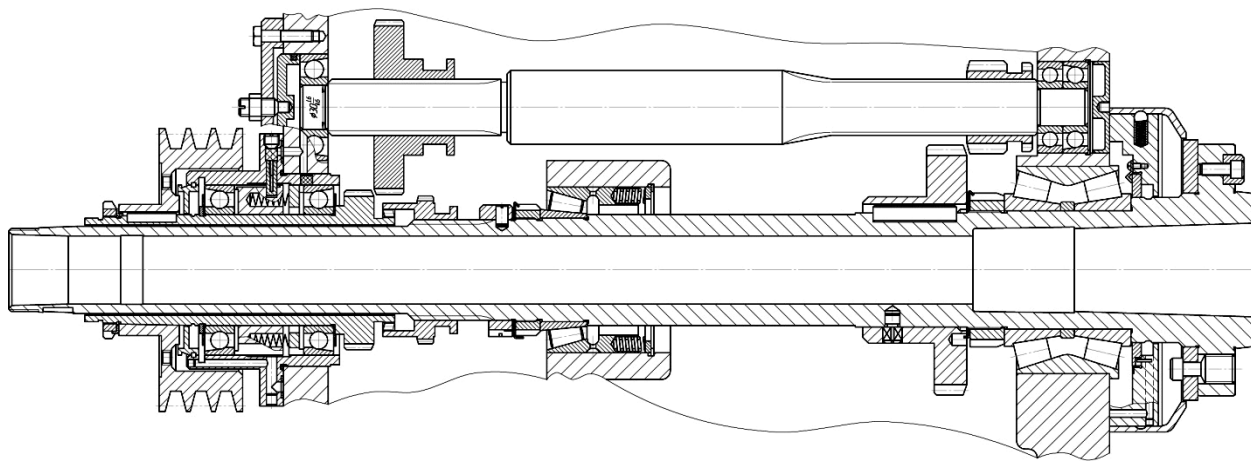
Конструкция шпиндельного узла токарного станка мод. 16B16T1
